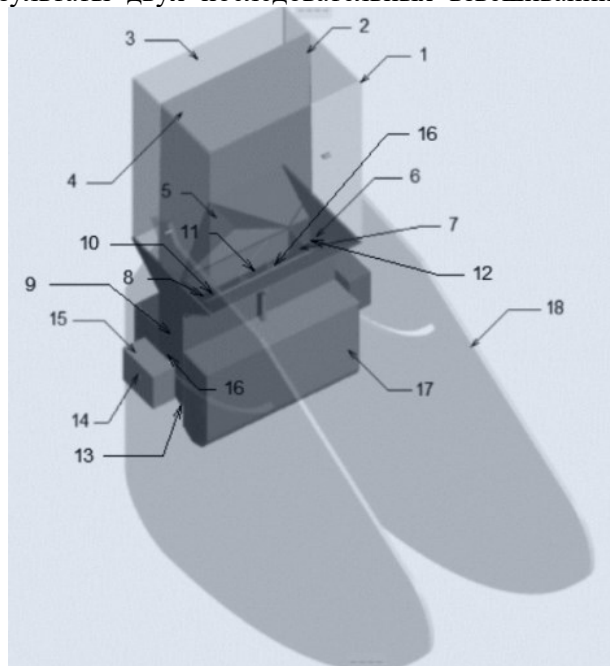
Формующее устройство для аддитивного изготовления многослойных стеновых конструкций:
